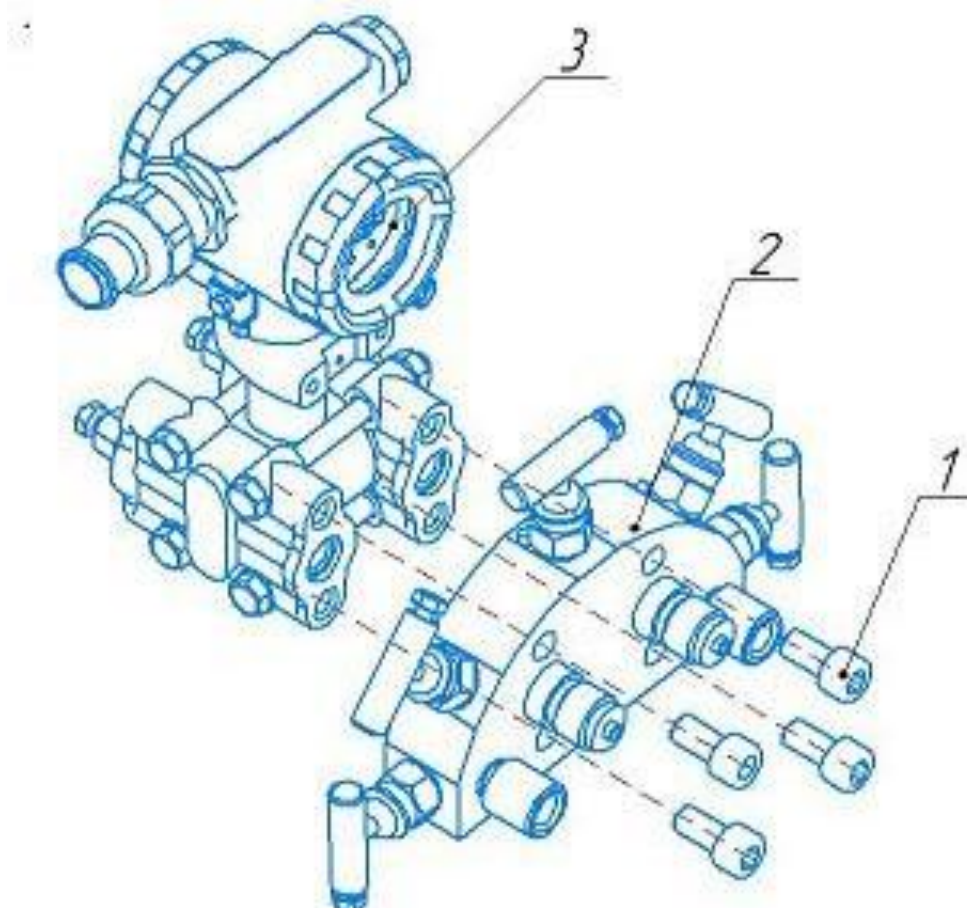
Схема сборки датчика с запорным клапаном типа КЗИЦ-23.05
